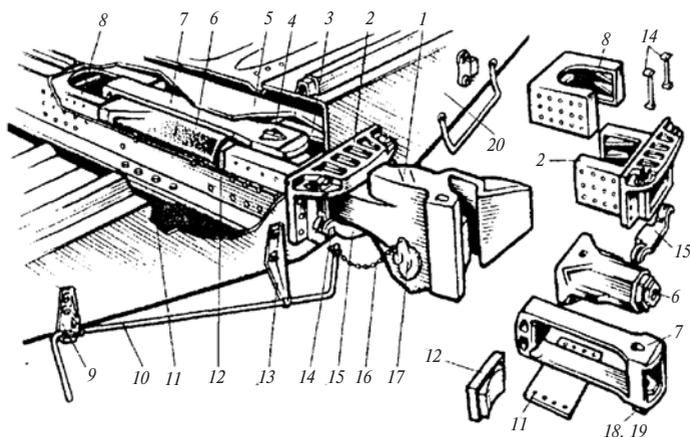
Расположение деталей автосцепного устройства вагона:
